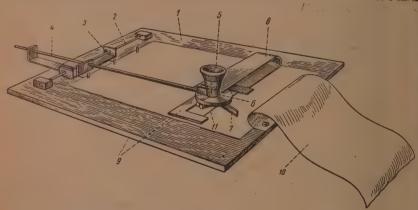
Общий вид прибора. 1— основная доска, 2, 4— рейки; 3— каретка; 5— головка; 6— муфта; 7— ножи; 8— скоба; 9— рамка; 10— верхний лист бумаги (отогнут); 11 — шнурок
